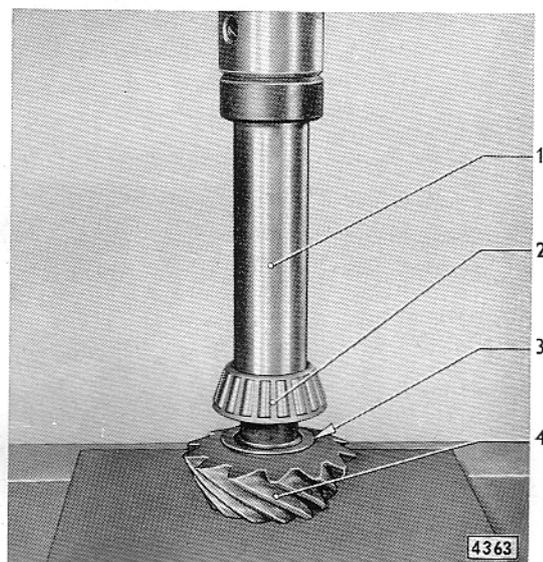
Inneres Antriebskegelradlager aufpressen
